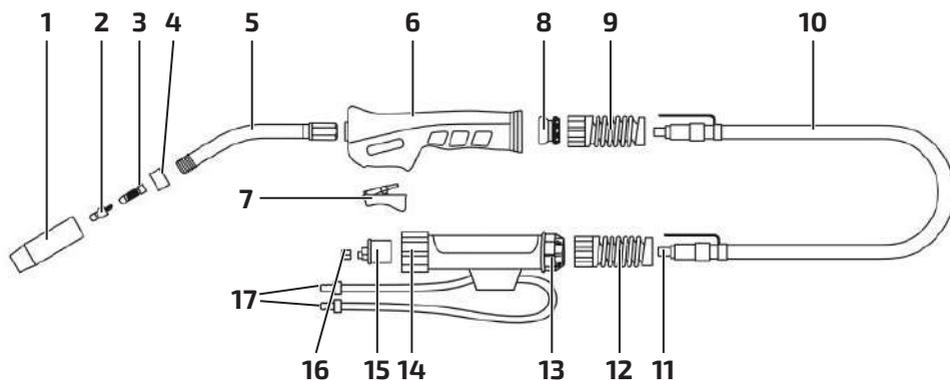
Схема горелки для MIG сварки.
